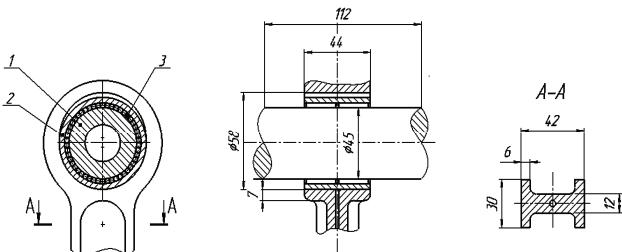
Конструкция узла ПГШ с игольчатым подшипником: 1 – поршневой палец; 2 – втулка; 3 – игольчатые ролики
